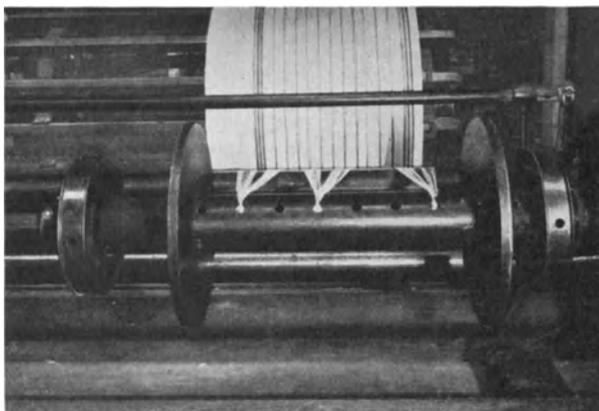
Bäummaschine mit leerem Kettenbaum, Kette am Kettenbaum in Bohrungen befestigt.
